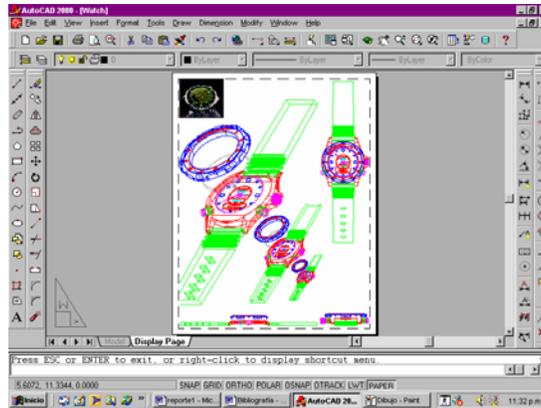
Ejemplo de ensamble en un diseño hecho en CAD
